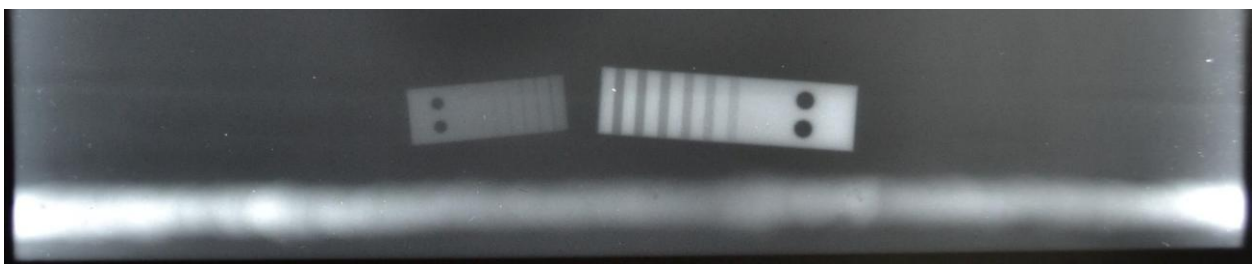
Радиографический снимок сварного образца из алюминия сваренного по установленной технологии
